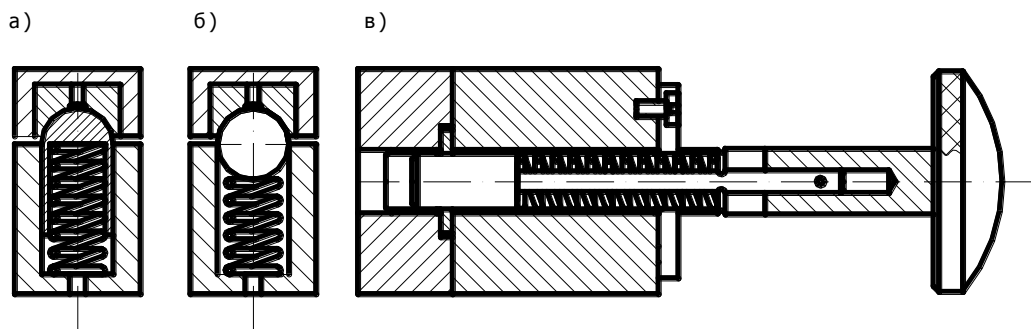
Примеры конструкции фиксаторов, применяемых в делительных устройствах: а – с погруженным пустотелым пальцем; б – с погруженным шариком; в – с вытяжным цилиндрическим пальцем: 1 – втулка; 2 – штифт; 3 – вытяжная кнопка; 4 – цилиндрический фиксатор.
